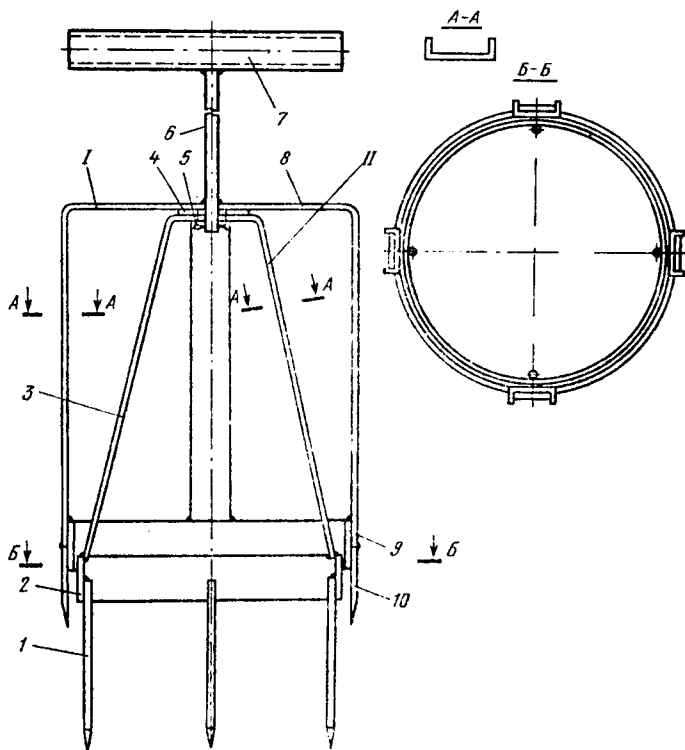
Четырехножовое устройство для обрезки кустов земляники:
